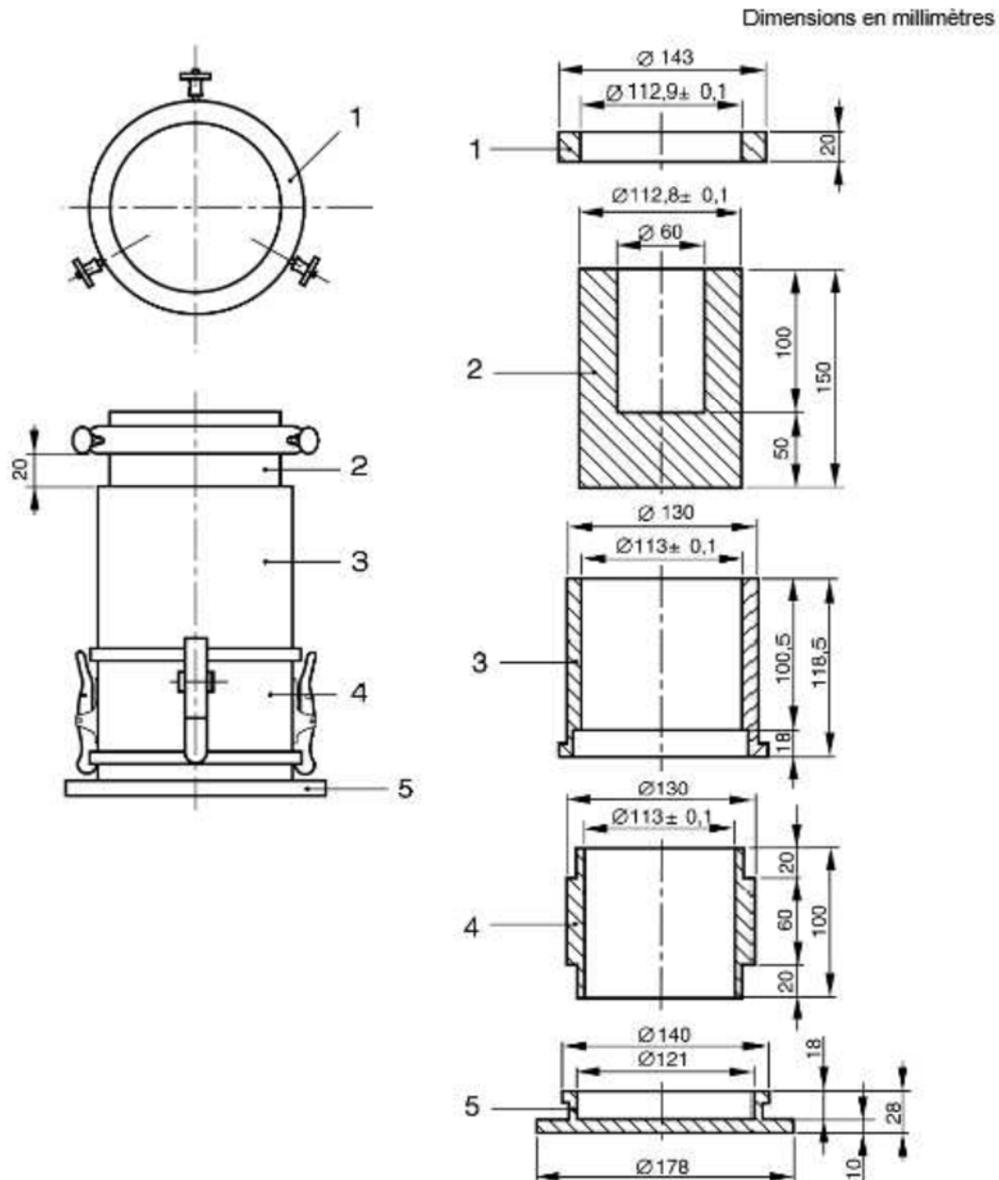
Dispositif d'essai de compression selon NF EN 13055-1
